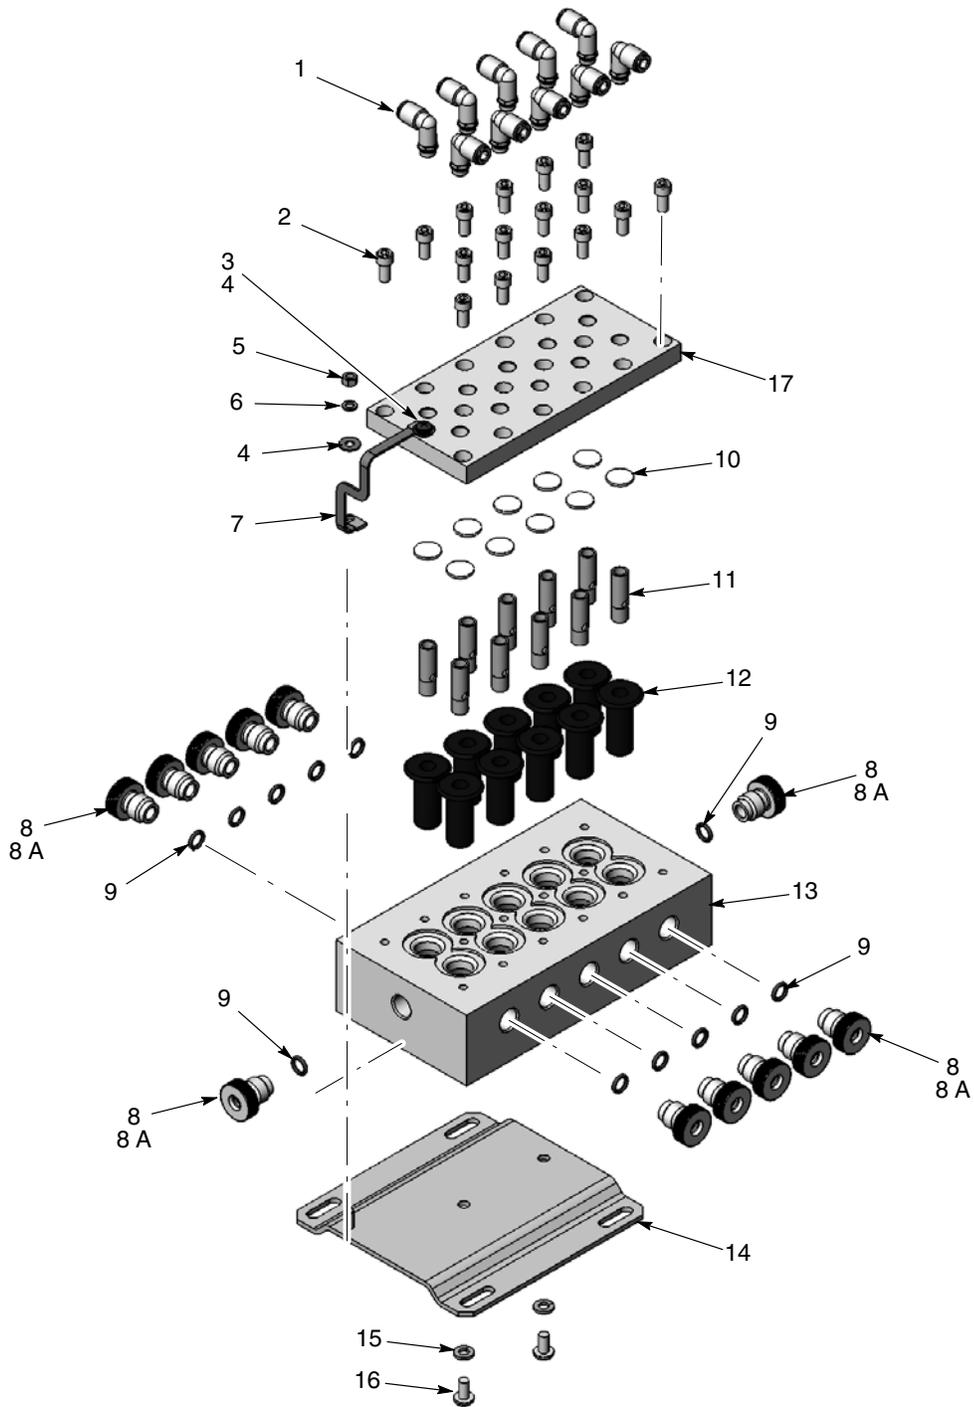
Explosionszeichnung des Verteilerblocks
